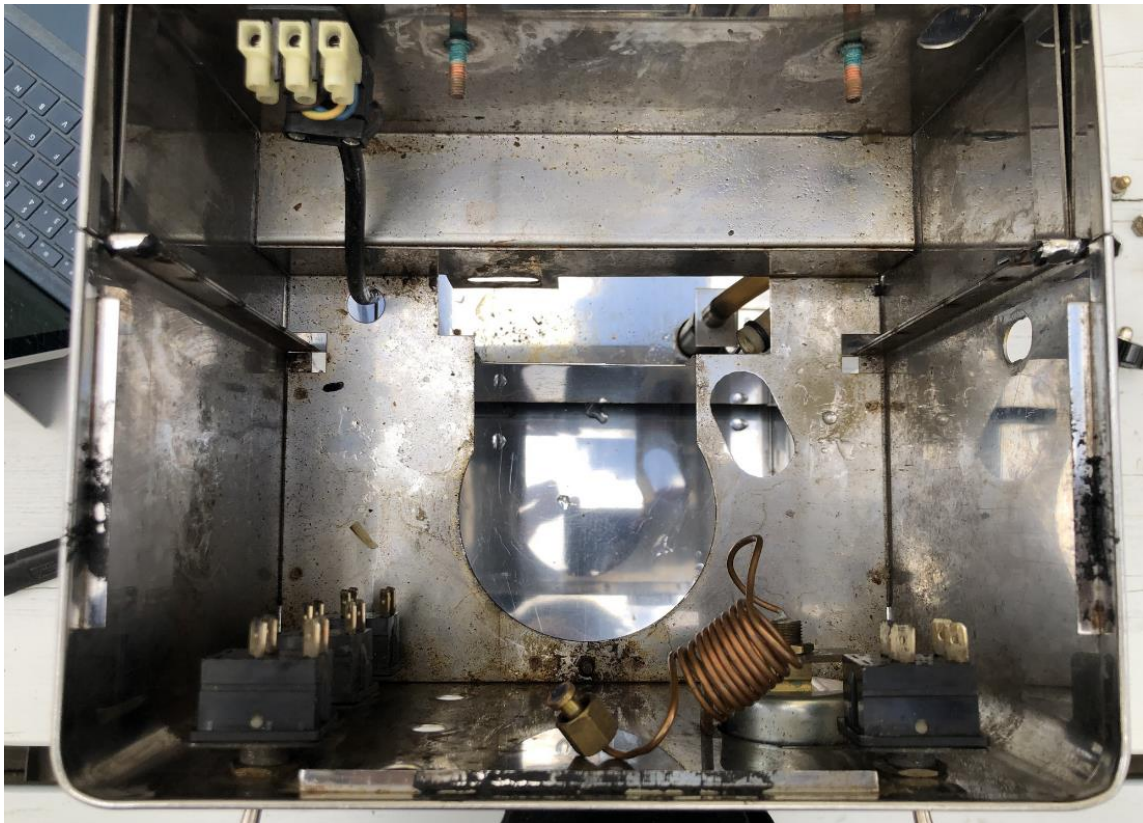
Leerer Innenraum der Kaffeemaschine
